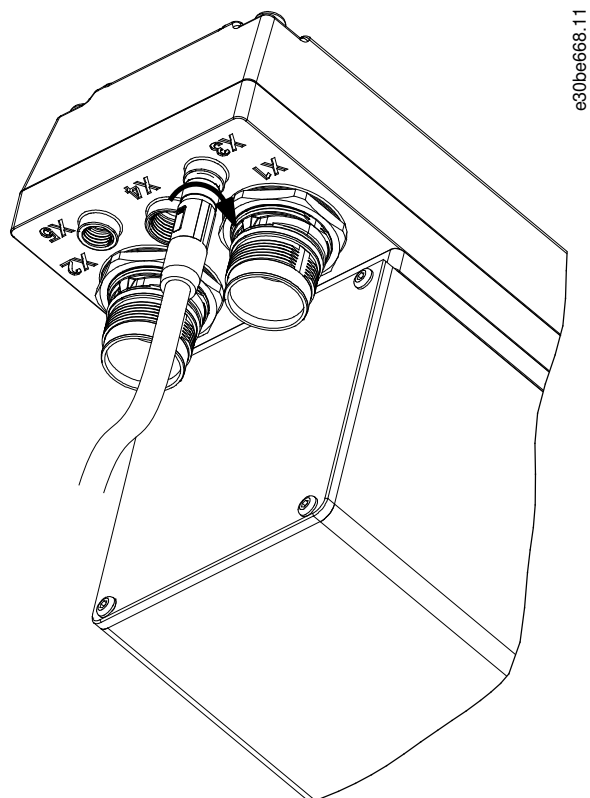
Collegamento del terzo cavo del dispositivo Ethernet
